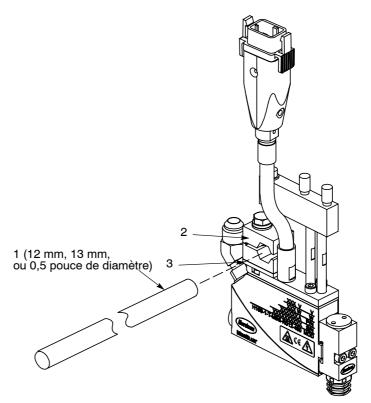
Montage d'un pistolet à l'aide de l'ensemble de serrage (la figure représente un pistolet mono-module ultra-plat)
